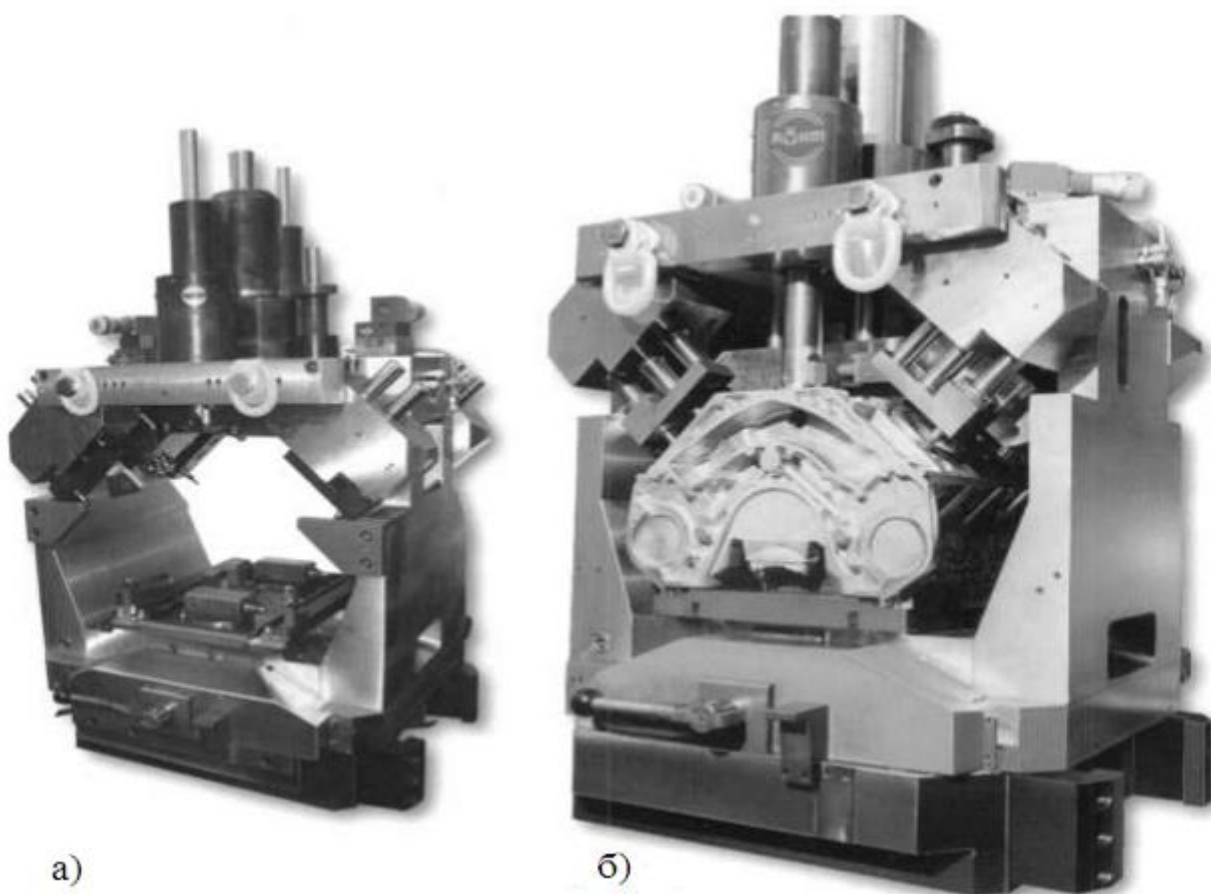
Зажимное устройство с гидравлическим приводом для зажима блоков двигателей а) без блока двигателя; б) с блоком двигателя.
